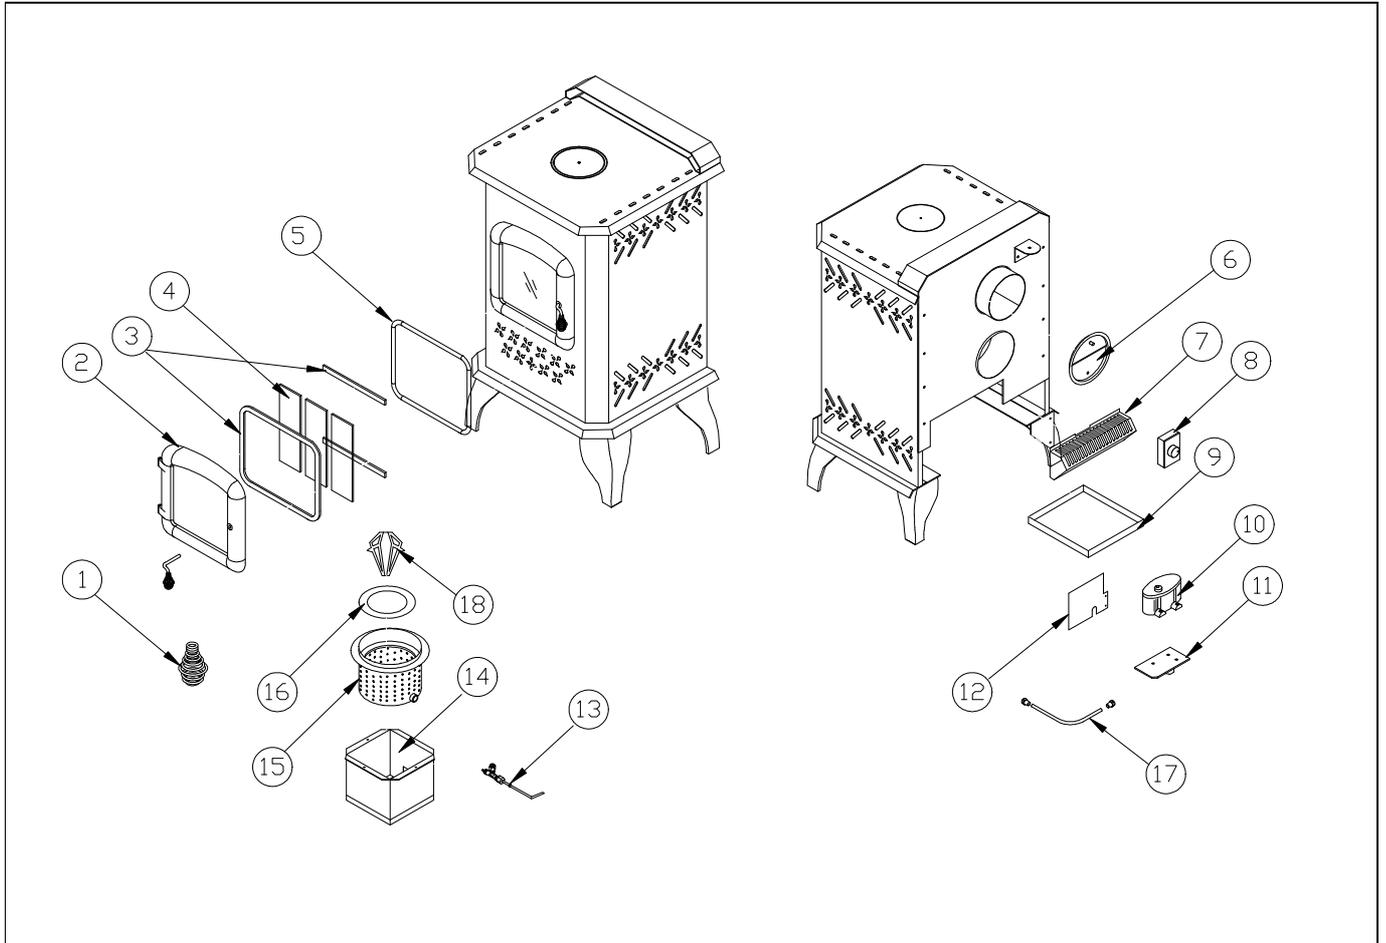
VUE EXPLOSÉE DU MONT BLANC, PIÈCES DE RECHANGE
